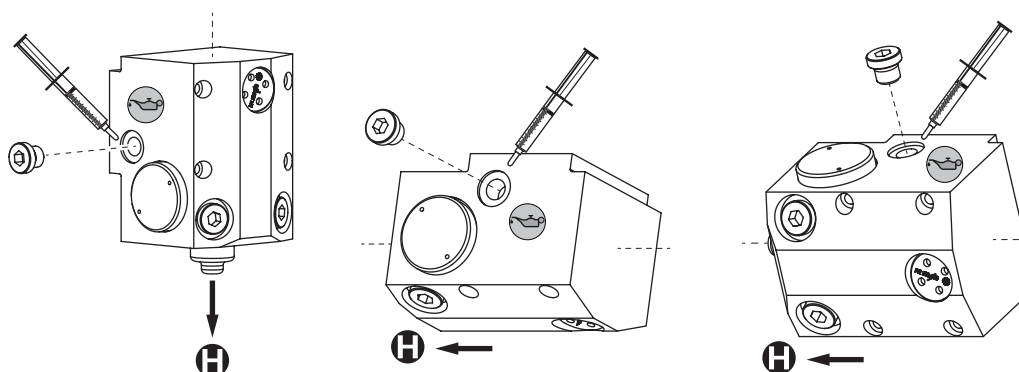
La posizione delle viti del dispositivo di riempimento dipende dall'orientamento di montaggio. Esempio: Versioni U
